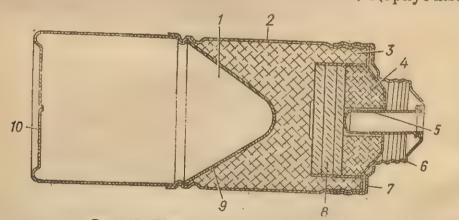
Корпус гранаты (в разрезе): 7 — кумулятивная выемка; 2 — оболочка; 3 — основной заряд; 4 — до-полнительный заряд; 5 — трубка; 6 — резьба; 7 — крышка; 8 — картонная прокладка; 9 — кумулятивная воронка; 10 — дно
